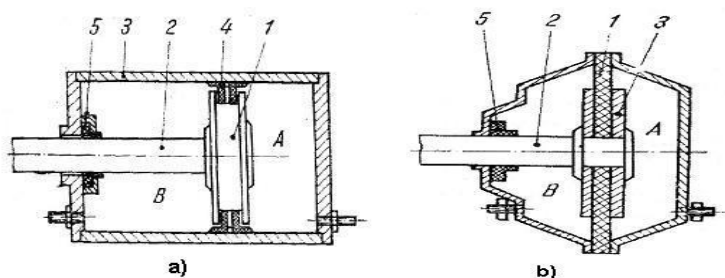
Cilindru cu piston (a) și cu membrană (b).
